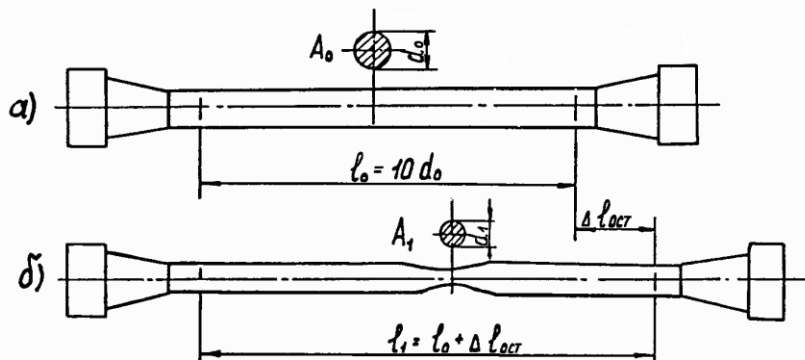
Эскиз цилиндрического длинного образца
